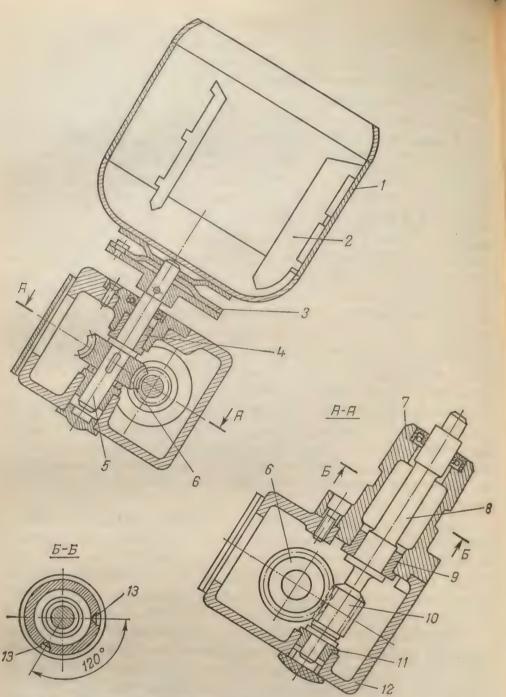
Механизм MC25-200 для перемешивания овощей при приготовлении салатов и винегретов
